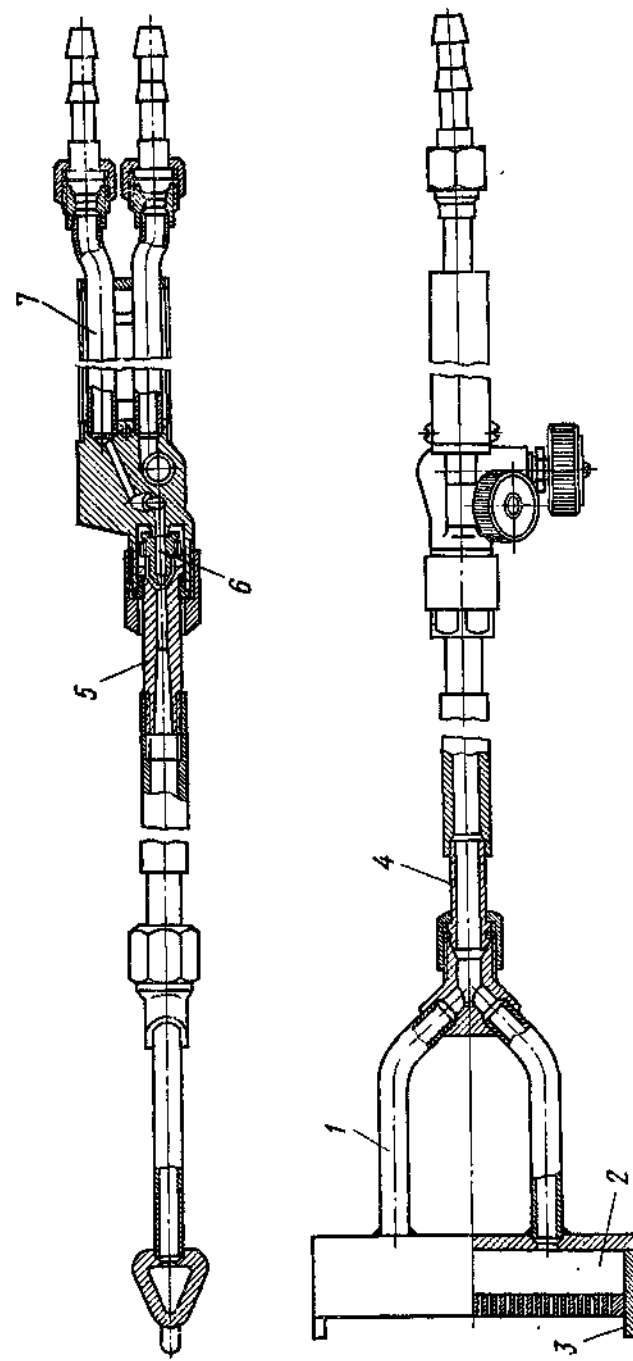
Многофакельная горелка для поверхностной очистки металла:
